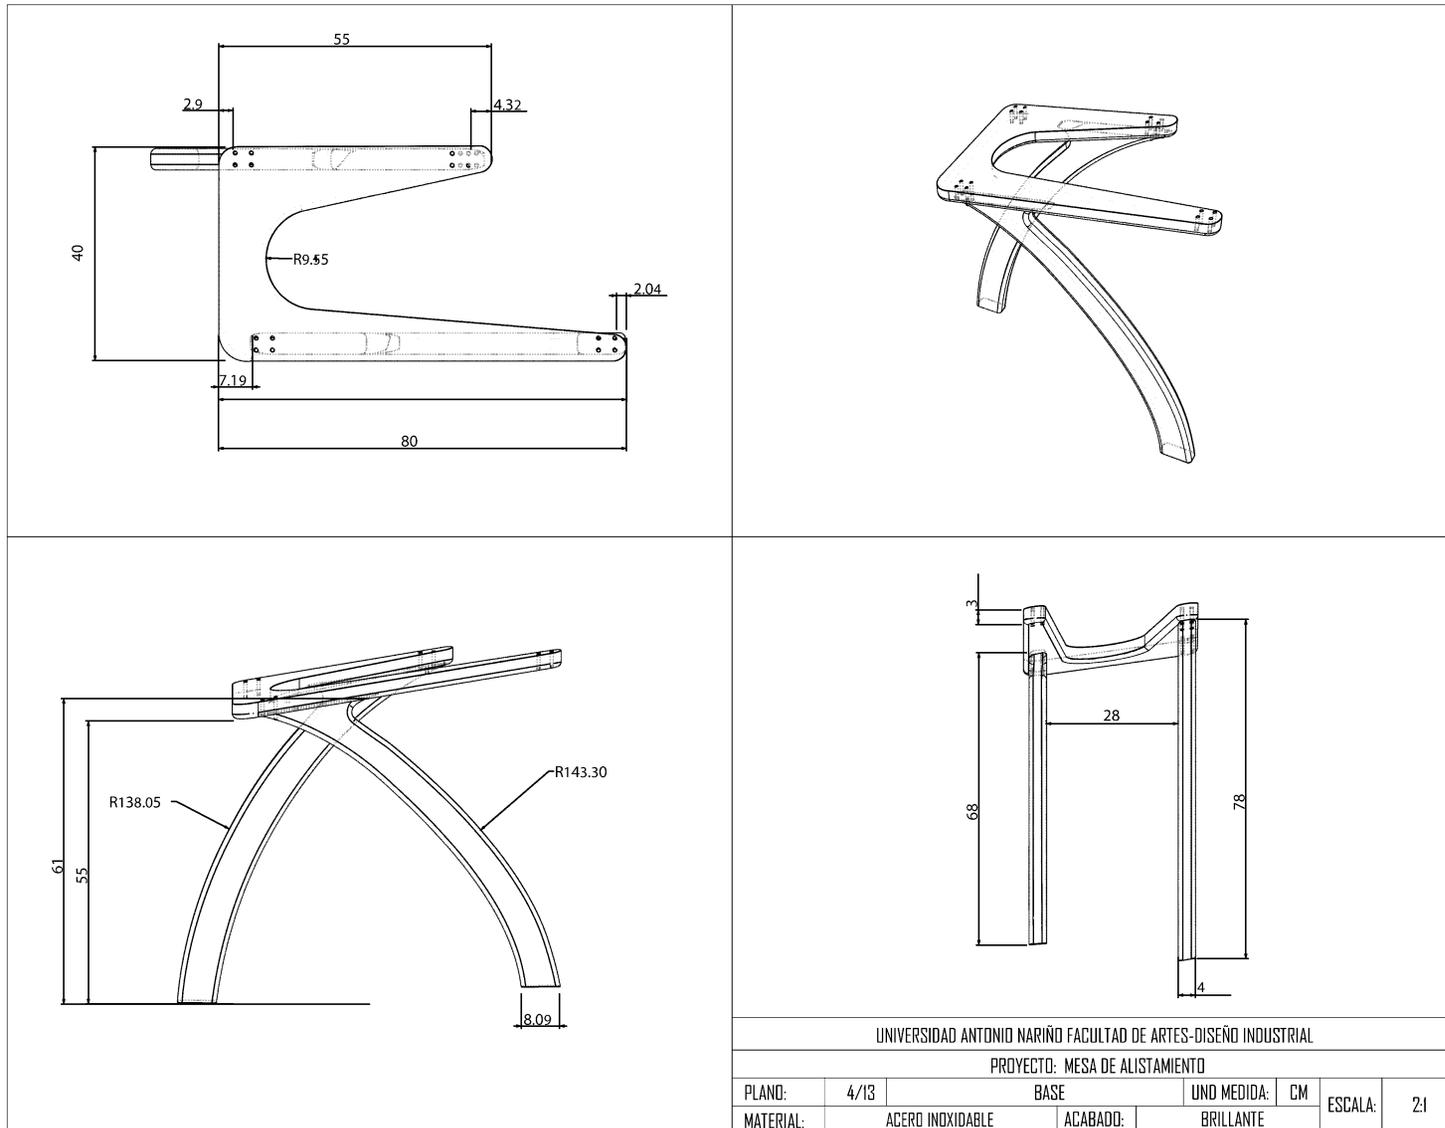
Planos piezas 3 (Elaboración propia, 2020)
